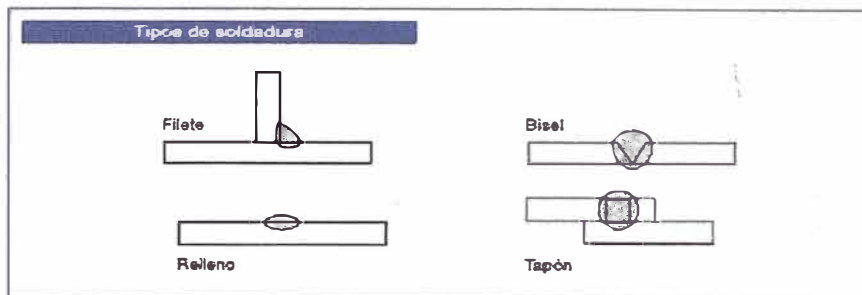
Tipos de soldadura (Fuente: Manual de Soldadura Indura)
